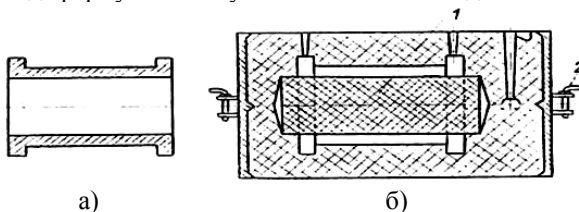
Ескіз виливка (а) і форма для його виготовлення (б)
